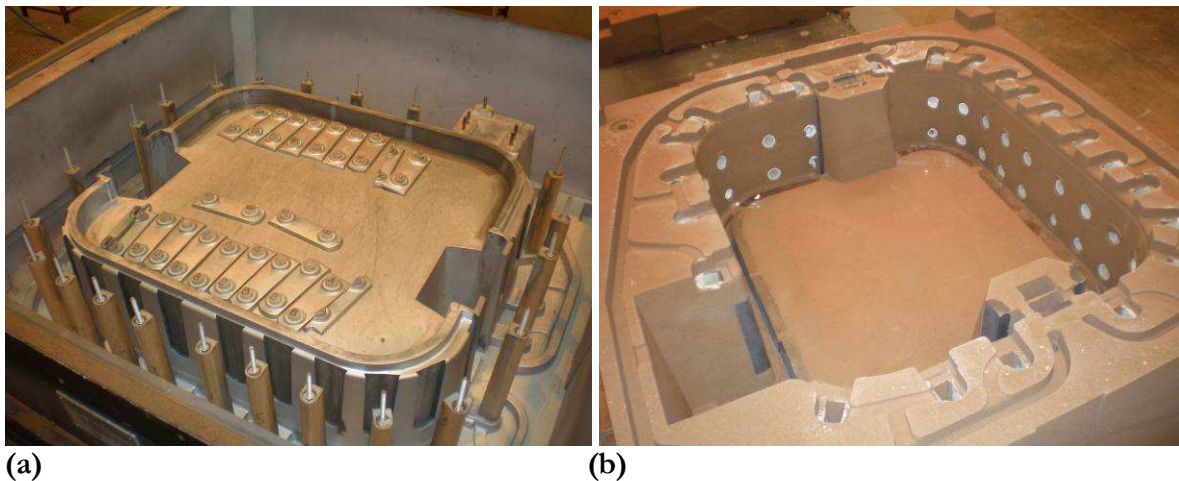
Boite de moulage (a) et moule (b) des deux pièces applicatives
